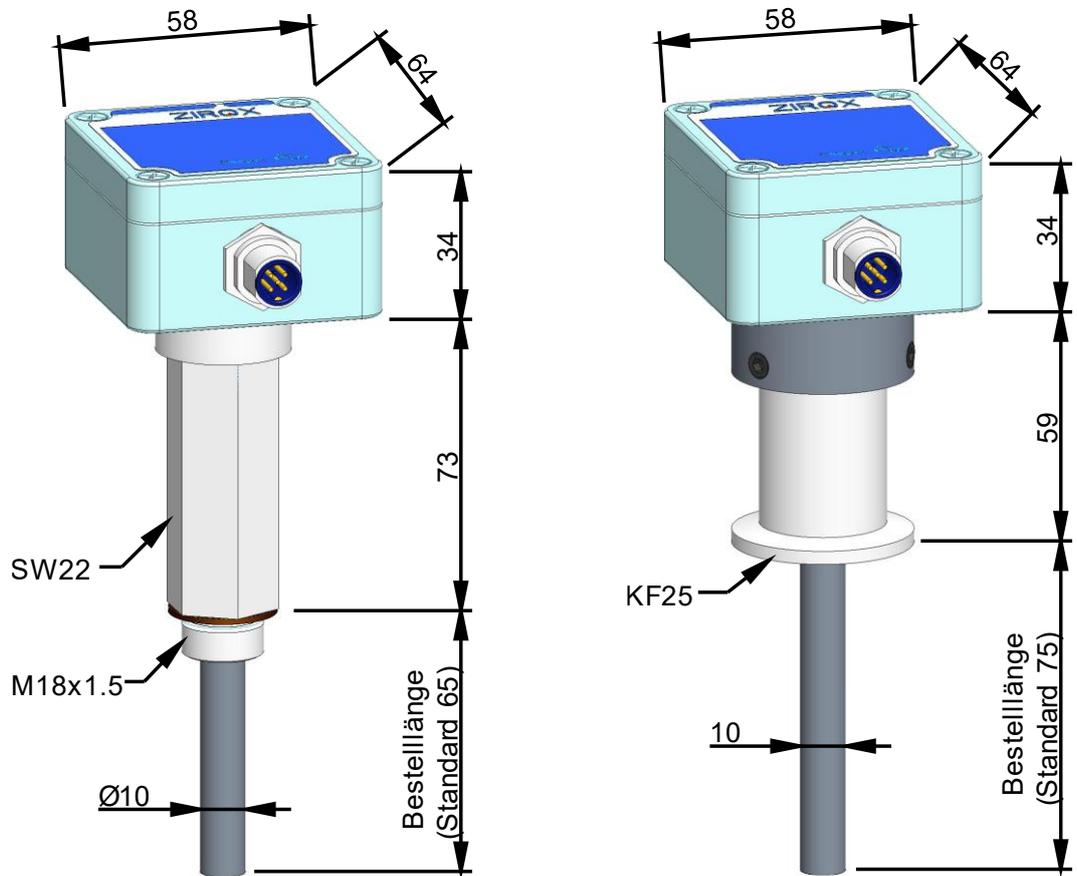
Maßzeichnung Sonde mit Einschraubgewinde (links) oder Flansch (rechts)
